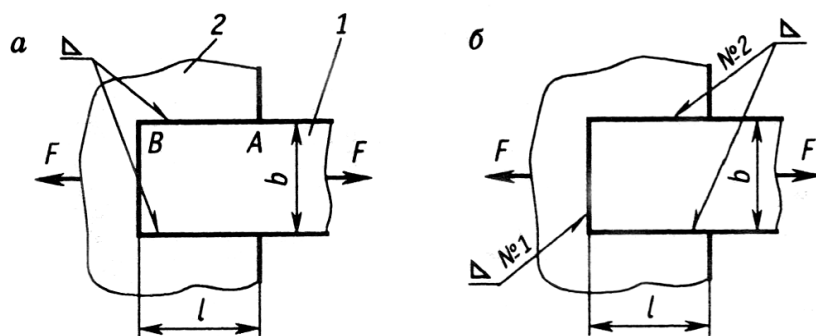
Сварное нахлесточное соединение:
